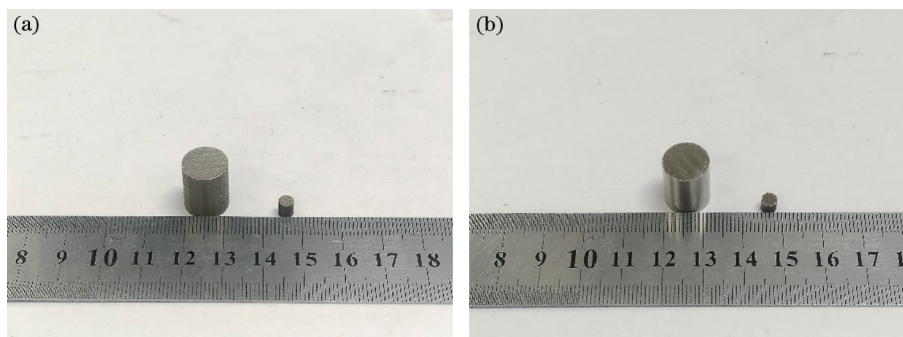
316L 不锈钢实物图。(a) SLM 316L; (b) 冷轧 316L
